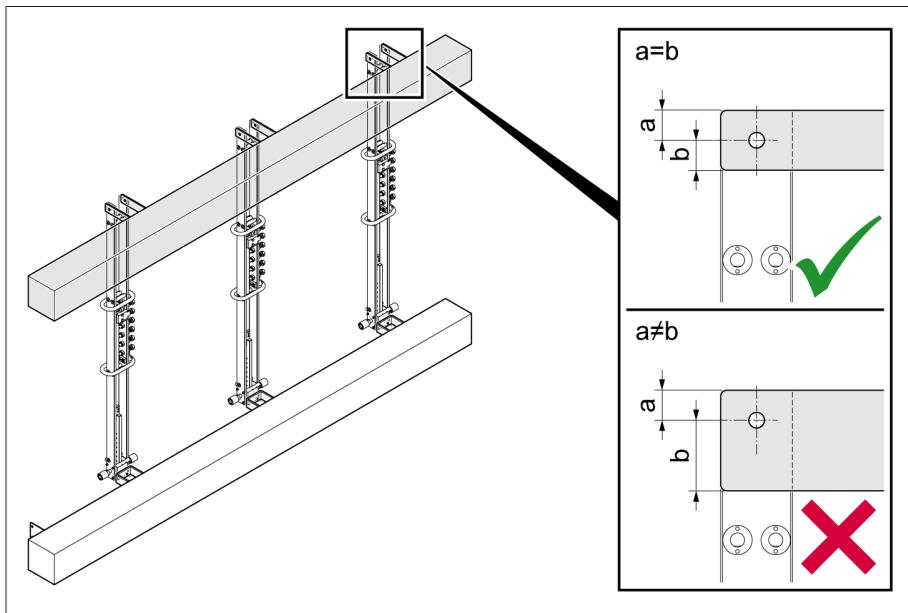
Крепежное приспособление на держателе, устройство ПБВ с боковым расположением контактов
